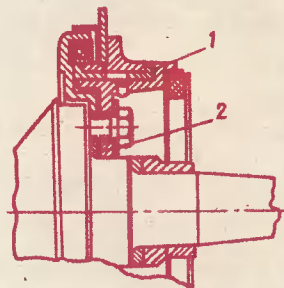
Установка шайбы в механизме переднего тормоза автомобиля «Москвич-401»: 1 — ремонтная шайба; 2 — регулировочные шайбы.
